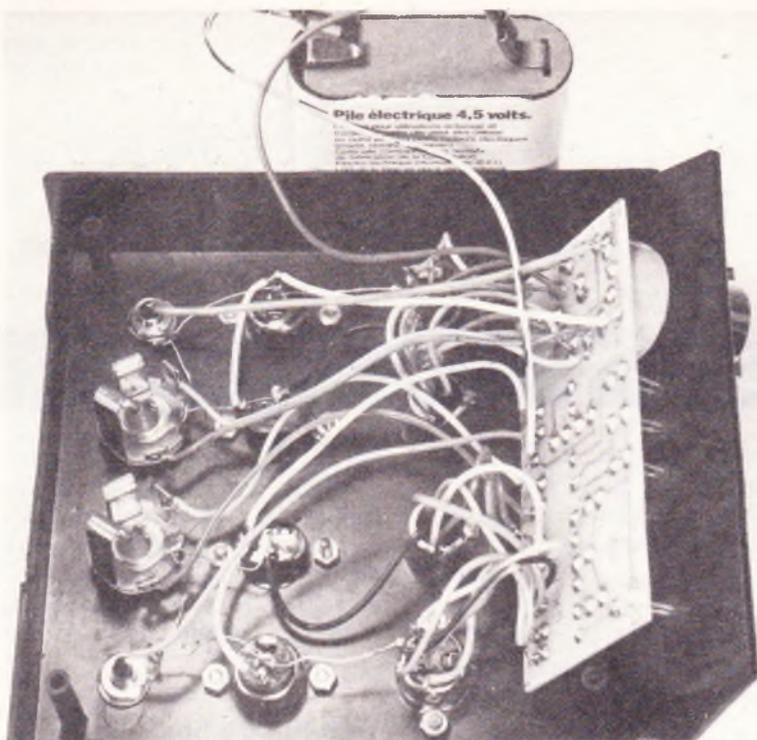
Le câblage des socles au module représente une soixantaine de soudures...
